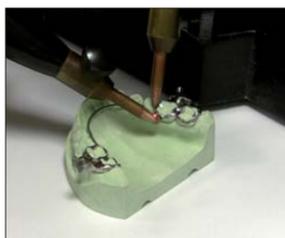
Den Lingual- und Palatinalbogen mittels Punktschweißen oder Laser fixieren.
